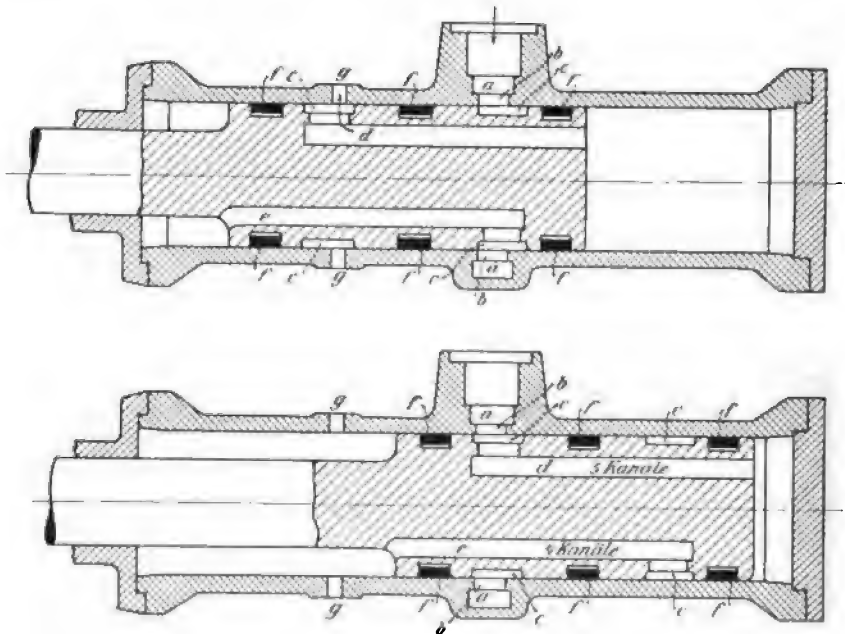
Steuerung der Triumph-Bohrmaschine der Ruhrthaler Maschinenfabrik.
